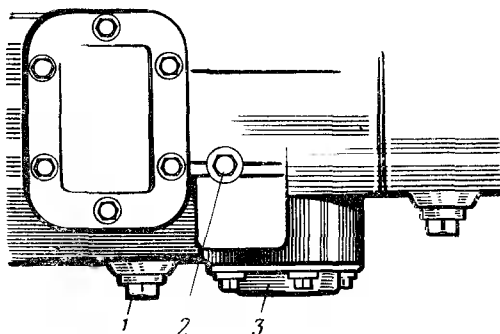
Пробки контрольного и сливного отверстий коробки передач:
